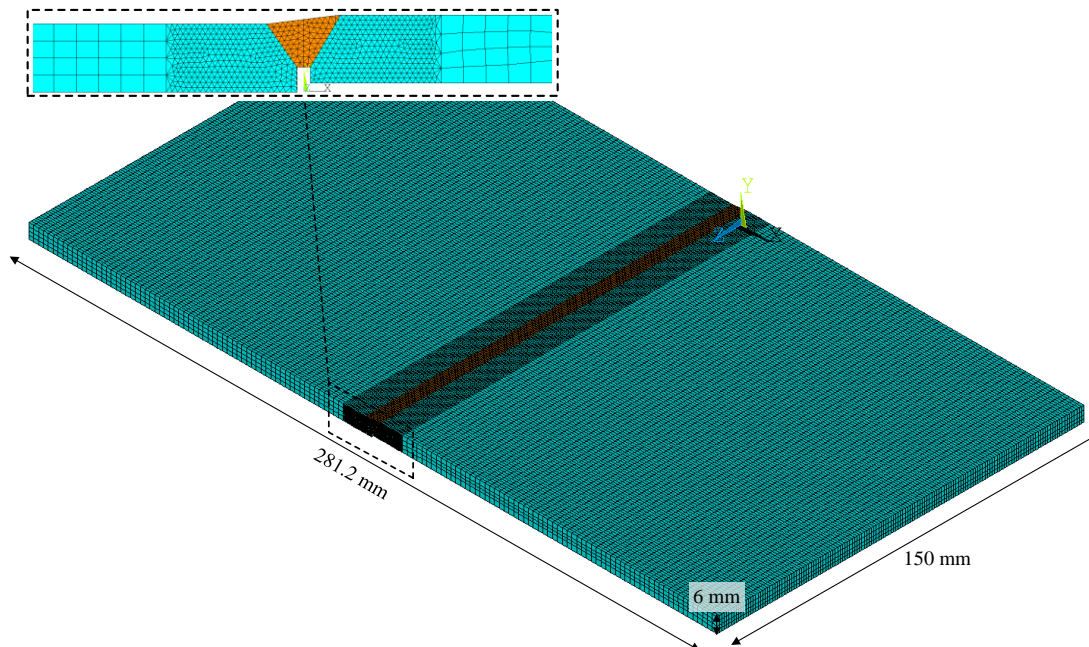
Maillage de l'éprouvette soudée bout à bout
